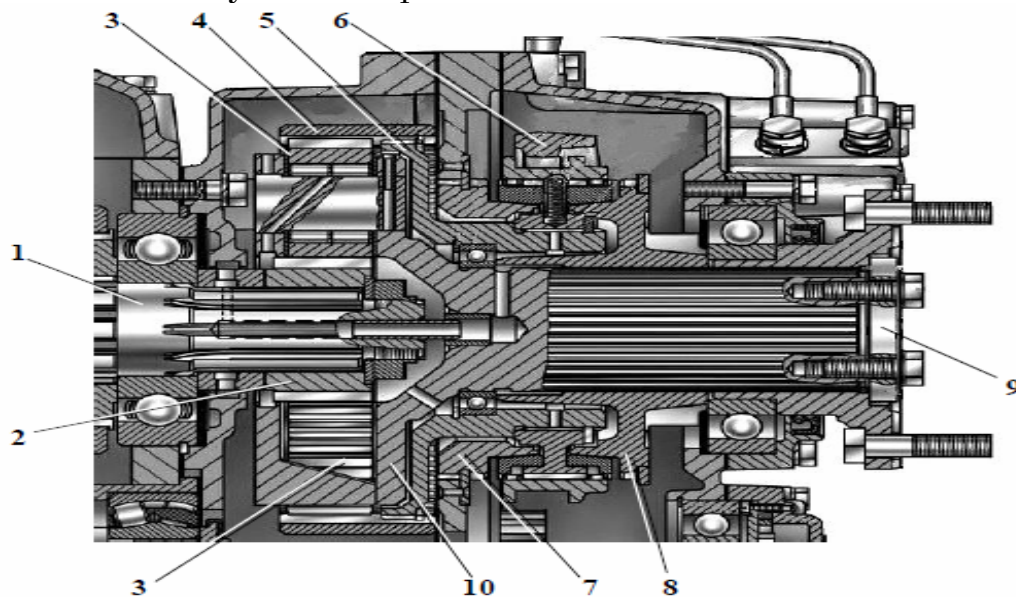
Демультипликатор коробки передач КАМАЗ модели 161:
